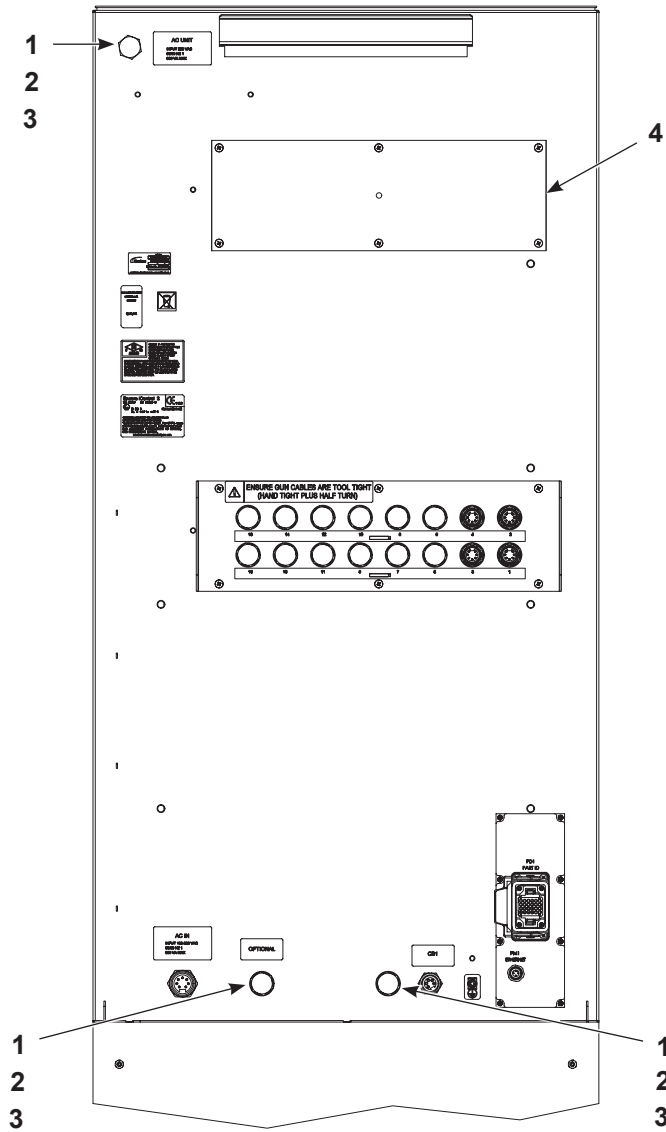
Piezas de las consolas principal y auxiliar; vista posterior (1 de 3)
